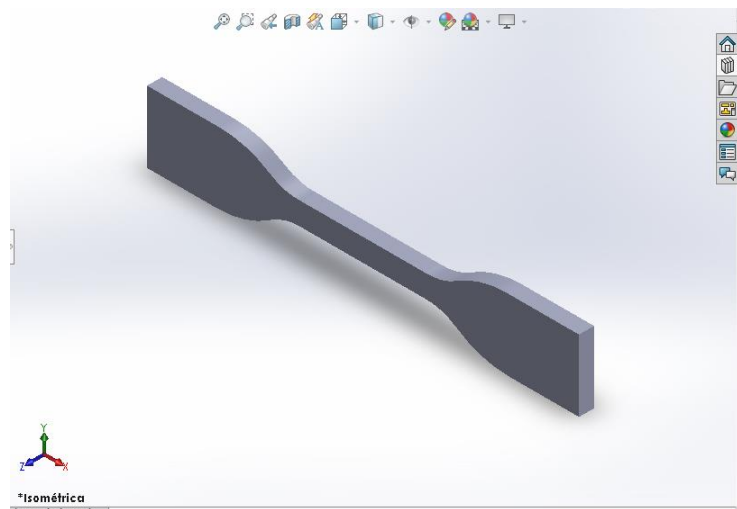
Diseño CAD de probeta para ensayo de tracción.
